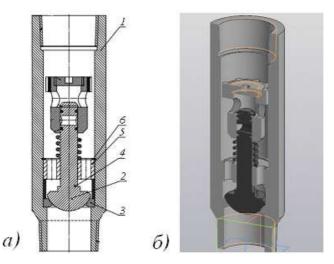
Обратный клапанный узел с каплевидной формой тарелки:
